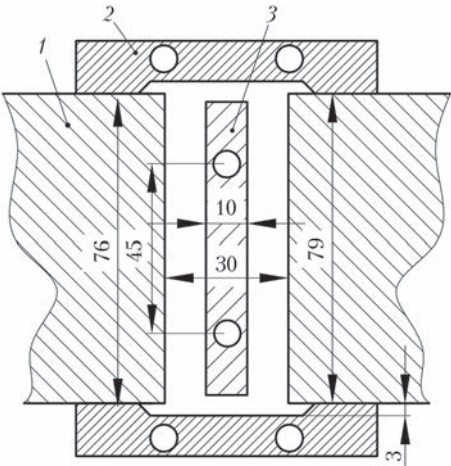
Геометрические параметры сборки изделий под ЭШС: 1 — свариваемые изделия; 2 — водоохлаждаемая формирующая планка (ползун); 3 — мундштук
